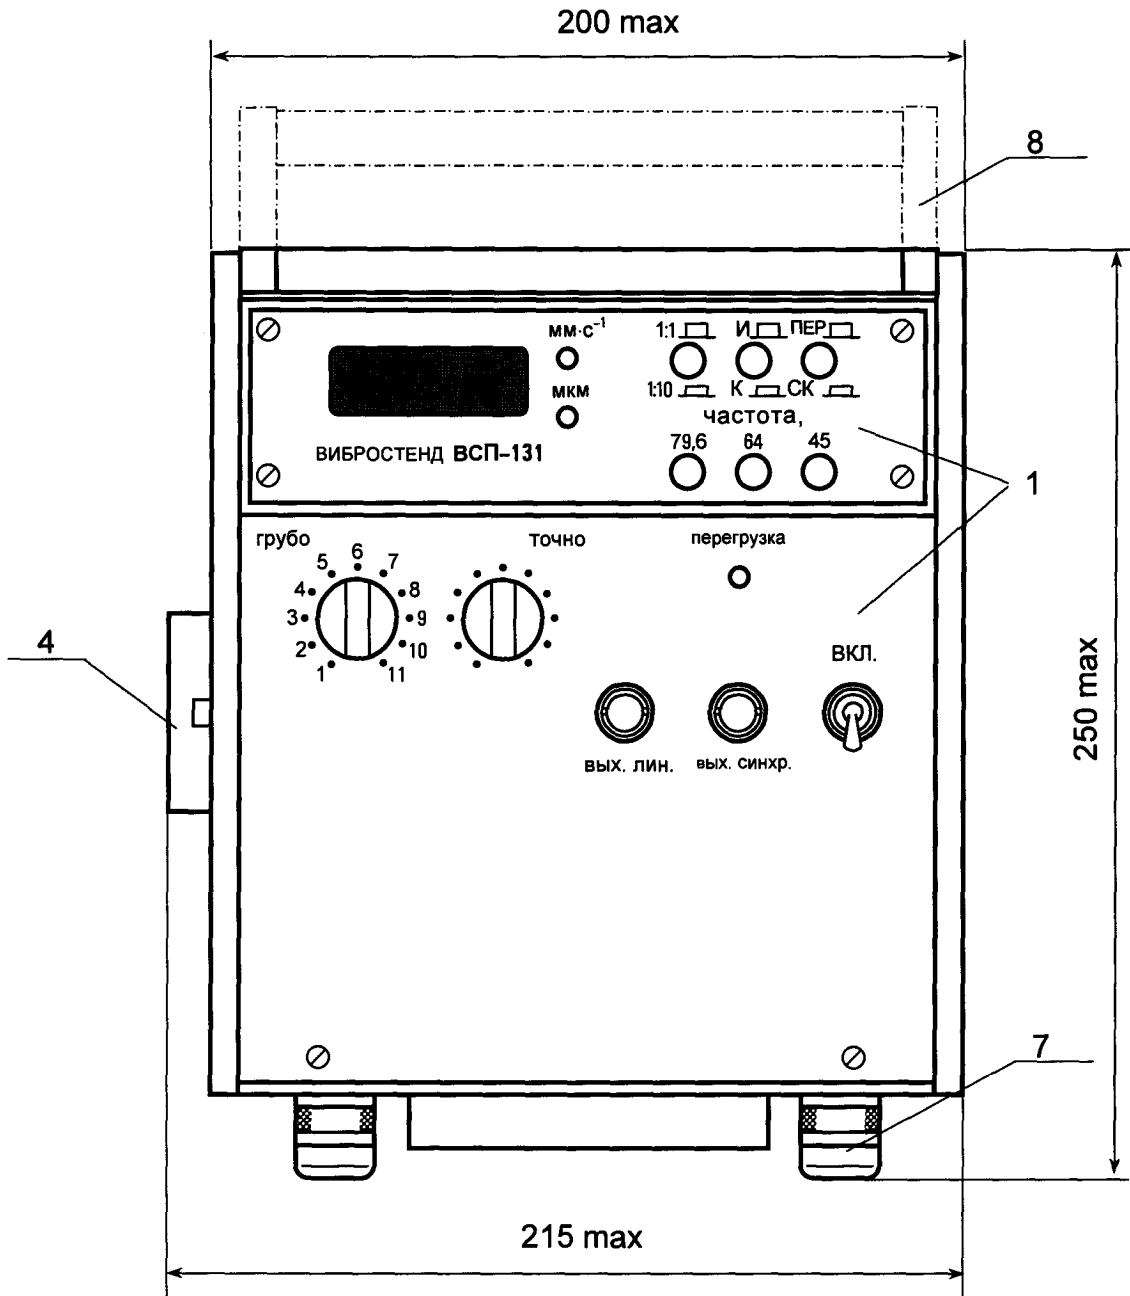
Внешний вид ( со стороны передней панели) и габаритные размеры вибростенда ВСП-131
